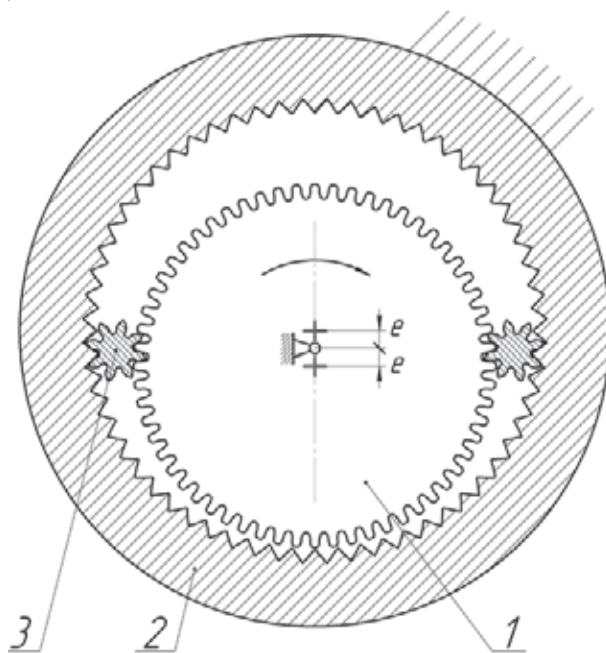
Роторная планетарная гидромашина с круглыми зубчатыми звеньями (RU 2513057 [3]): 1, 2 – центральные зубчатые колеса; 3 – сателлиты
